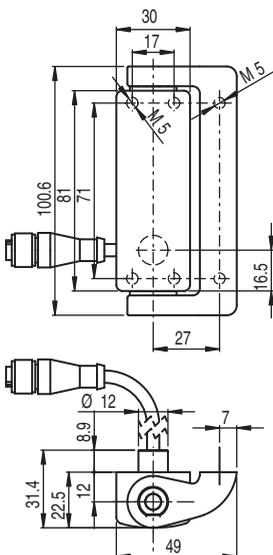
Dimensões do S400-Mx-CB02M12-W em mm
